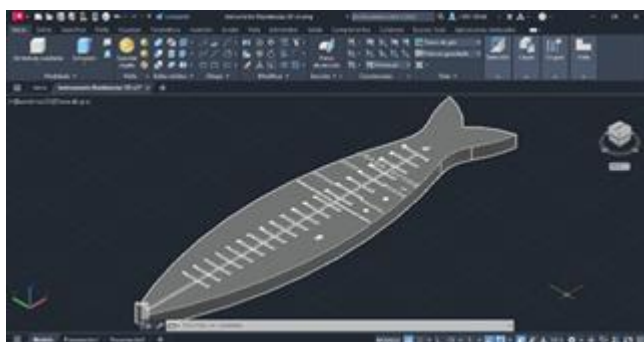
Sistema Poka Yoke que facilite la utilización del instrumento. Fuente: Elaboración propia.
